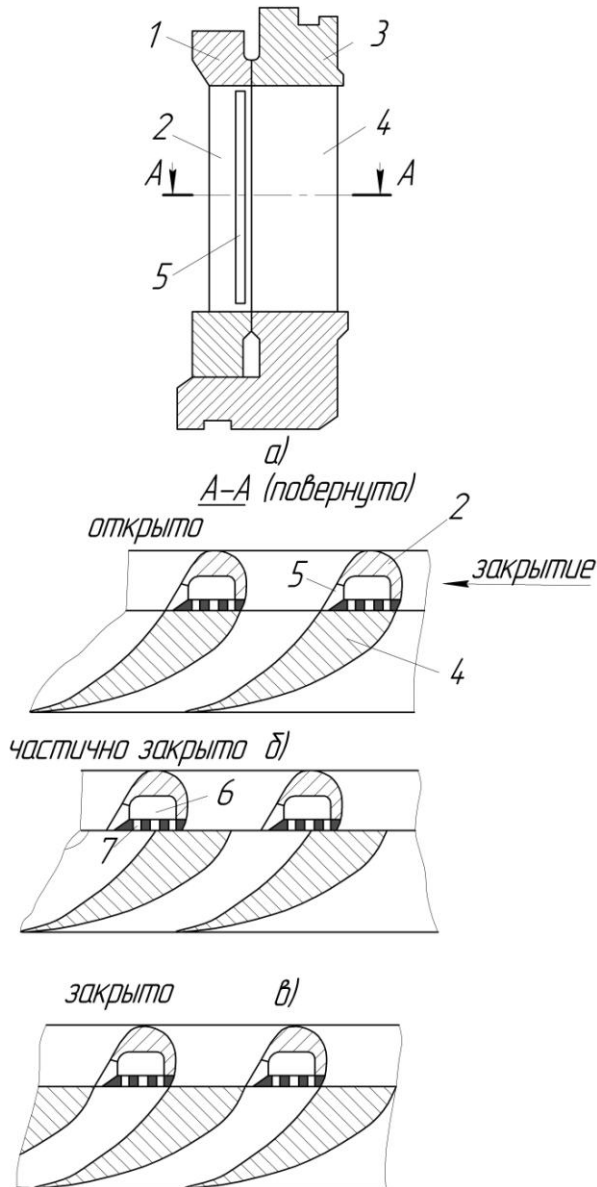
Конструкция усовершенствованного варианта поворотной диафрагмы:
